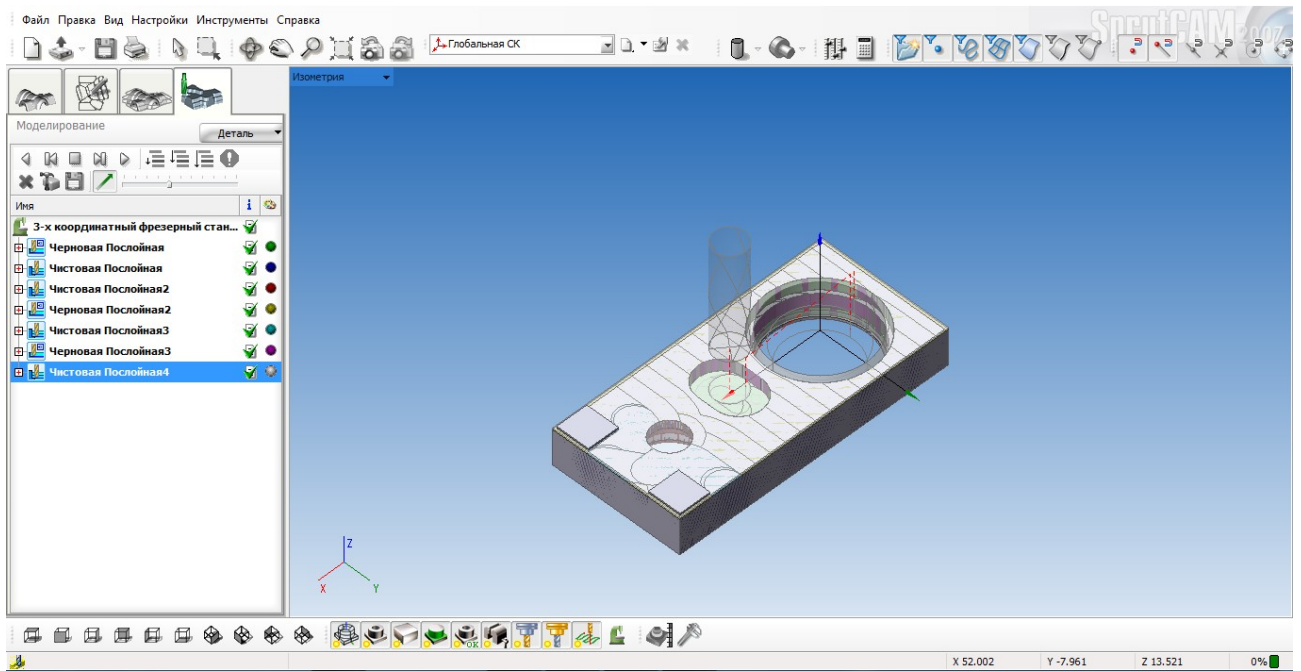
Моделювання чистового фрезерування отвору та пазу
